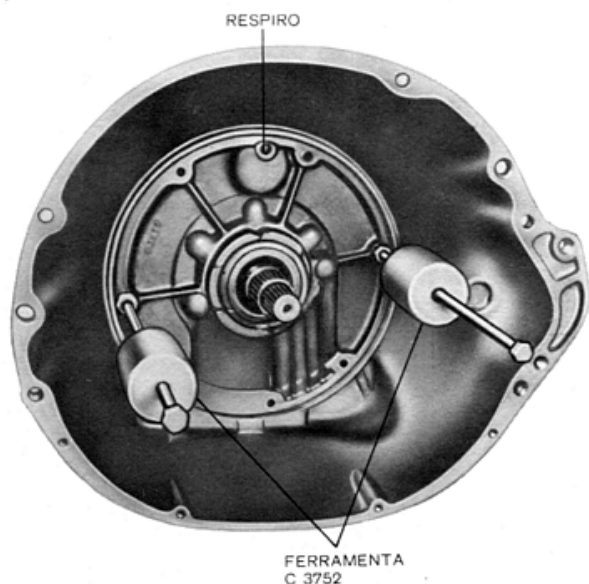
Remoção do conjunto da bomba de óleo e suporte do eixo de reação
